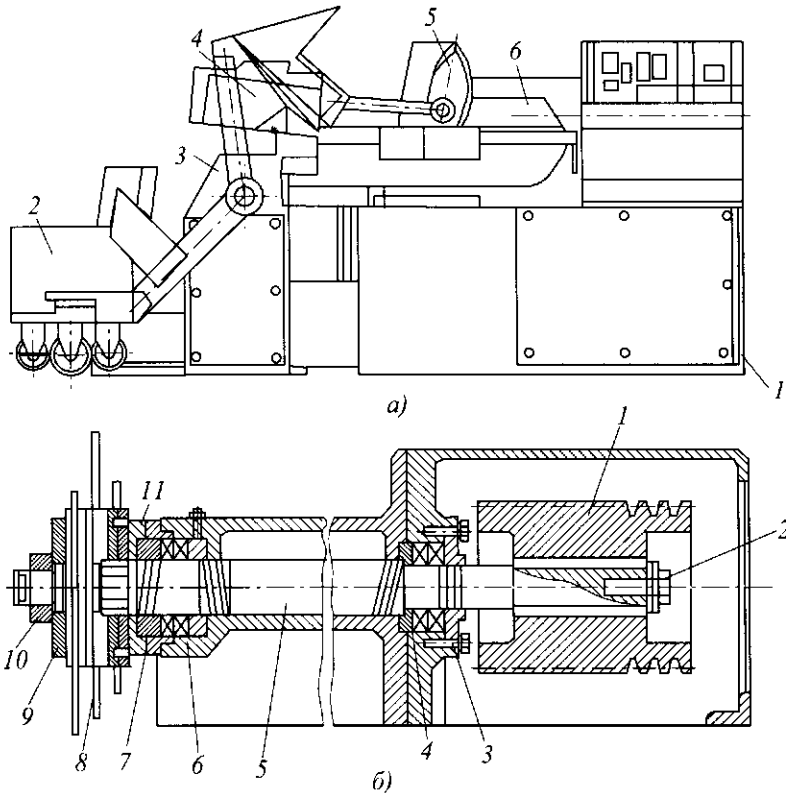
Куттер Л5-ФКМ: а – общий вид; б – ножевой вал
